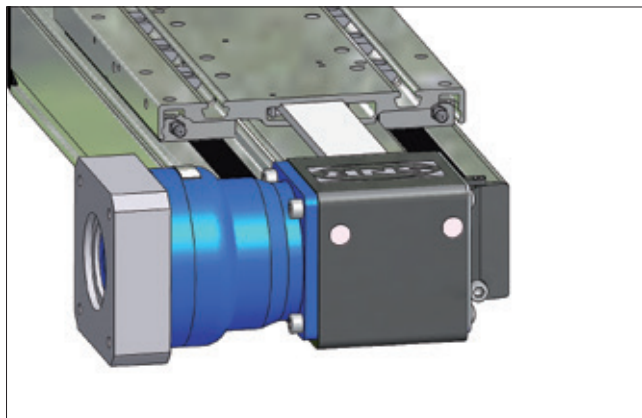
AXDL mit integriertem Planetengetriebe
